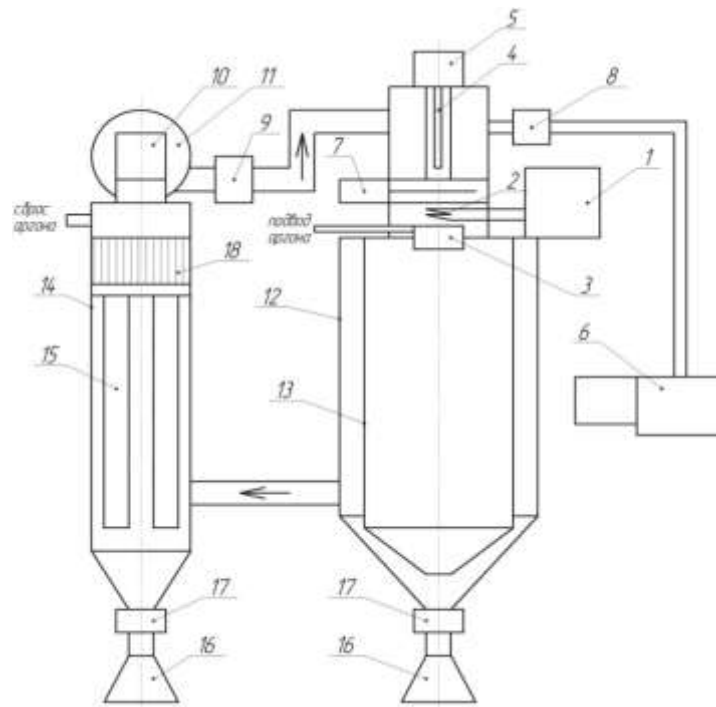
Схема УРМ-002: 1 – плавильный агрегат, 2 – индуктор, 3 – распылительная форсунка, 4 – заготовка, 5 – привод подачи заготовки, 6 – вакуумный насос, 7 – вакуумный затвор, 8,9,10 – вакуумные клапаны, 11 – циркуляционный вентилятор, 2 – камера распыления, 13 – экран, 14 – фильтровально-охлаждающая камера, 15 – рукавный фильтр, 16 – емкость для сбора порошка, 17 – блок вентиля, 18 – охладитель аргона
